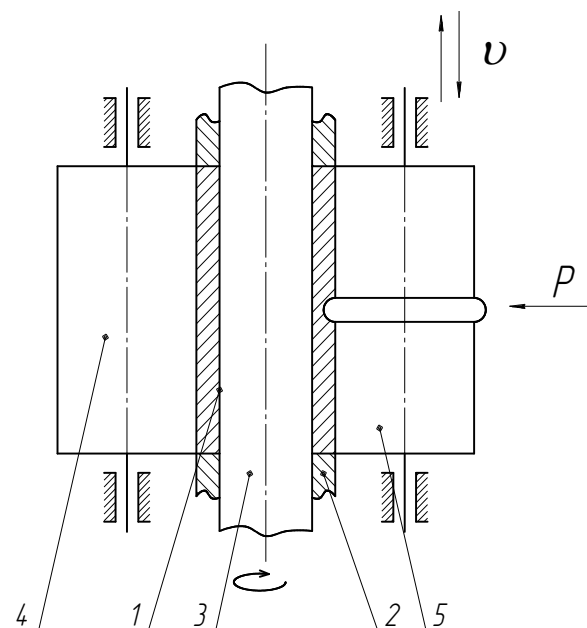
Схема обкатки формирующим и заглаживающим инструментом:
